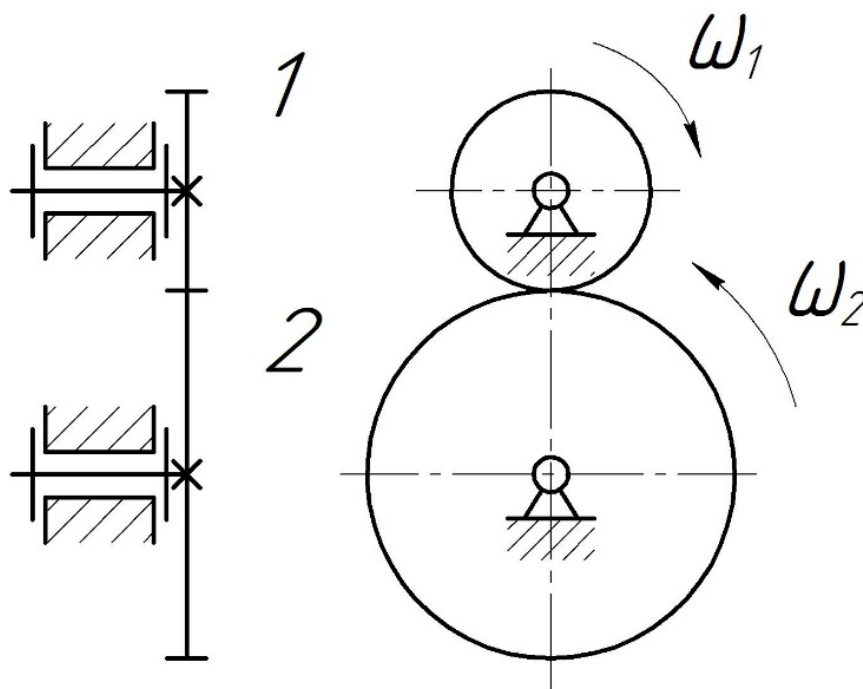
Схема цилиндрической зубчатой передачи внешнего зацепления
